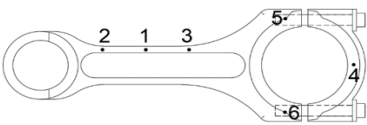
Hasil pengukuran *Clearance oil connecting Rod* = 0.50 mm (standart 0.63 – 0.75 mm)
